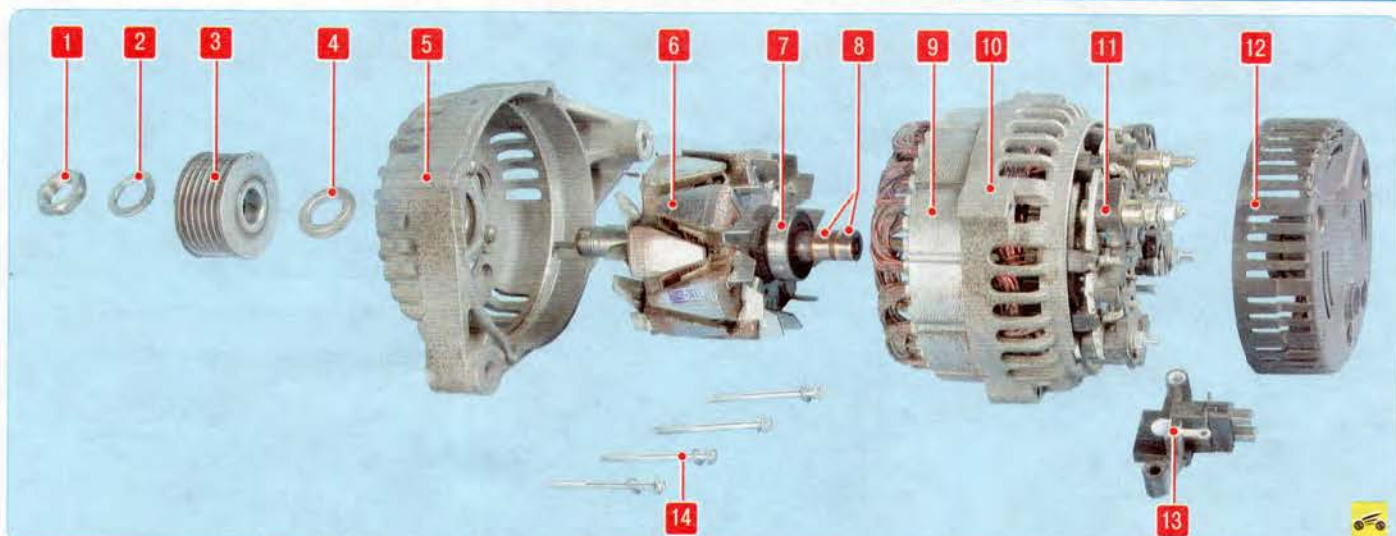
Детали генератора: 1 – гайка крепления шкива; 2 – шайба; 3 – шкив; 4 – втулка; 5 – передняя крышка; 6 – ротор; 7 – задний подшипник; 8 – контактные кольца; 9 – статор; 10 – задняя крышка; 11 – выпрямительный блок; 12 – кожух; 13 – щеткодержатель; 14 – стяжной болт
